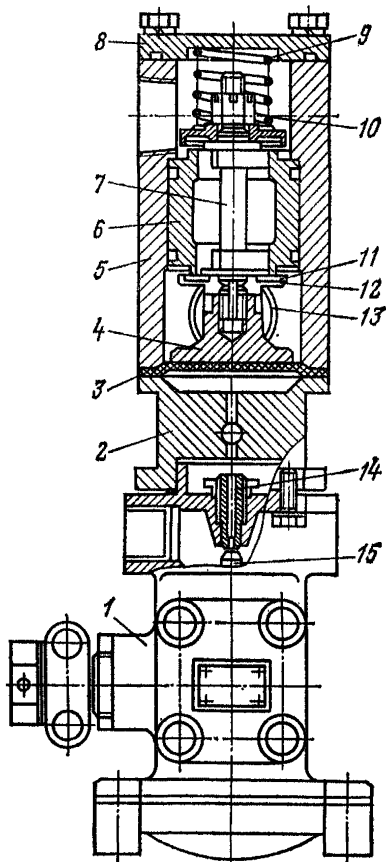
Взрывозащищенный электромагнитный клапан:
